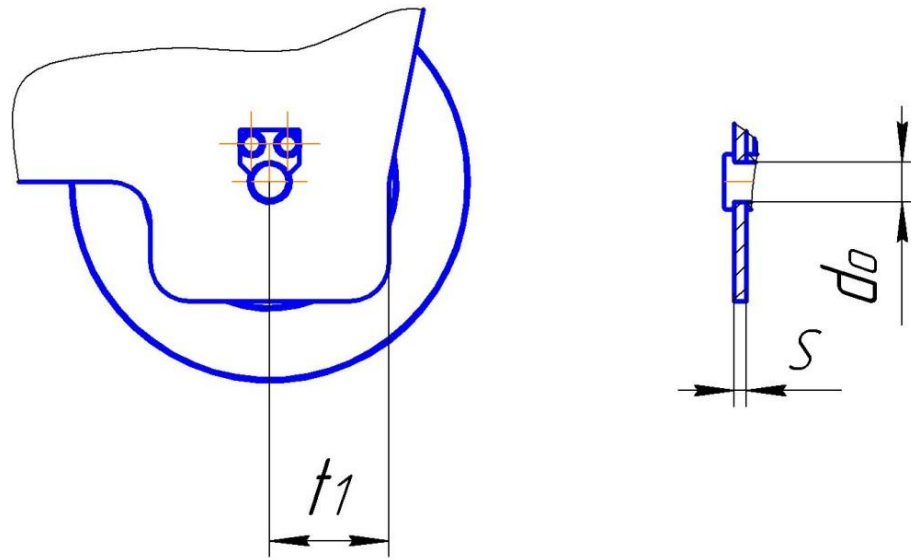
Розрахункова схема навантажень на щоки корпусу.
